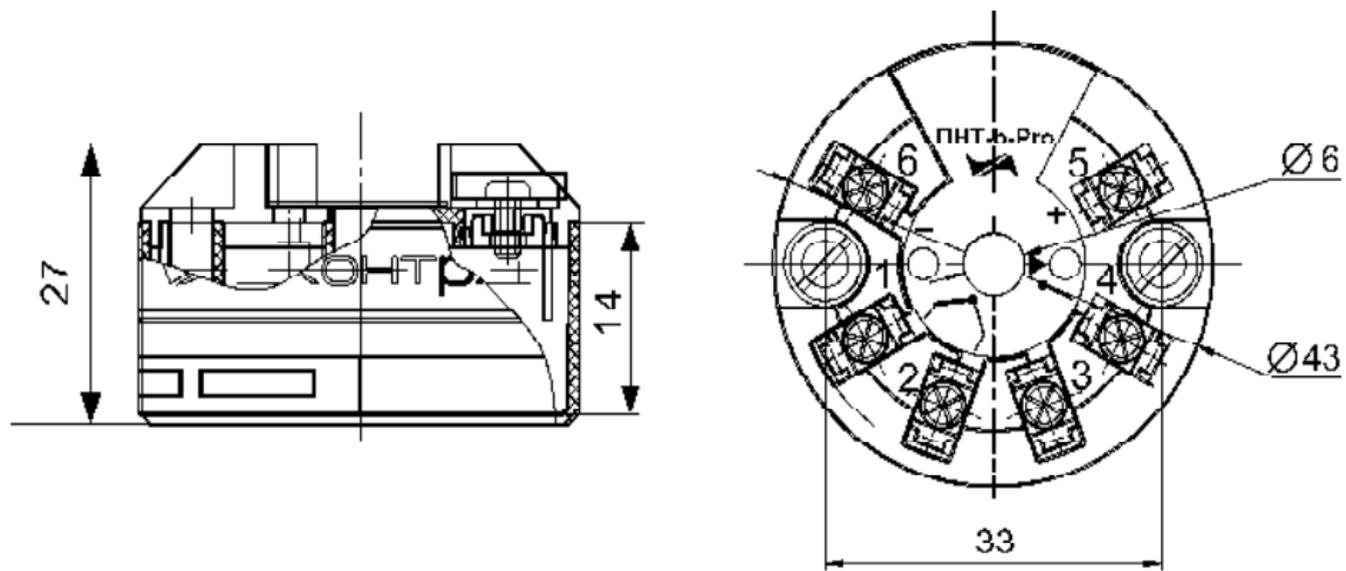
Внешний вид и габариты преобразователя ПНТ-b-Pro
